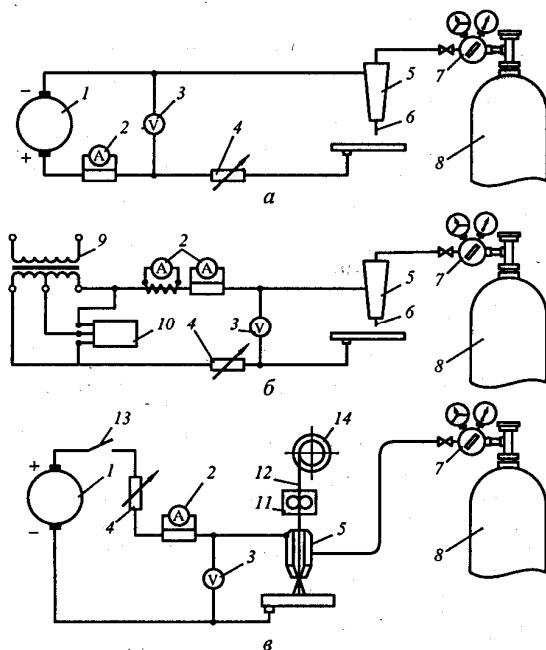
Схемы сварки в защитных газах:
